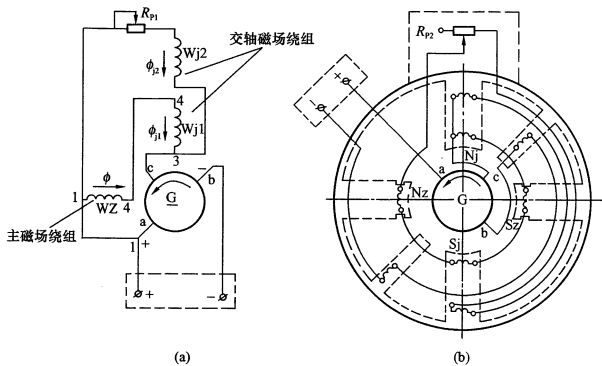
AX-320 型直流弧焊机电气线路
